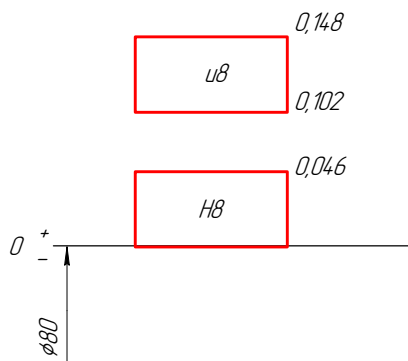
Схема расположения полей допусков посадки с натягом
